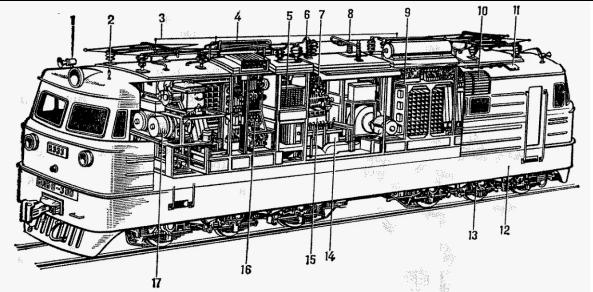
Электровоз: 1 — тифон; 2 — свисток; 3 — антенна; 4 — змеевик; 5 — сглаживающий реактор; 6 — разрядник; 7 — групповой переключатель; 8 — главный выключатель; 9 — выпрямительная установка; 10 — жалюзи; 11 — крышка песочницы; 12 — кузов; 13 — тележка; 14 — тяговый трансформатор; 15 — переходные реакторы; 16 — реверсор; 17 — вспомогательные машины.
